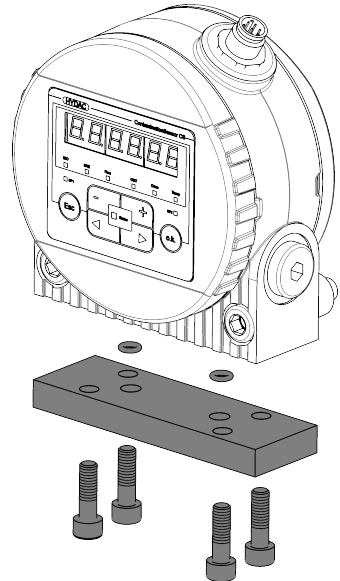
Montage auf eine Anschlussplatte mit Flanschanschluss
